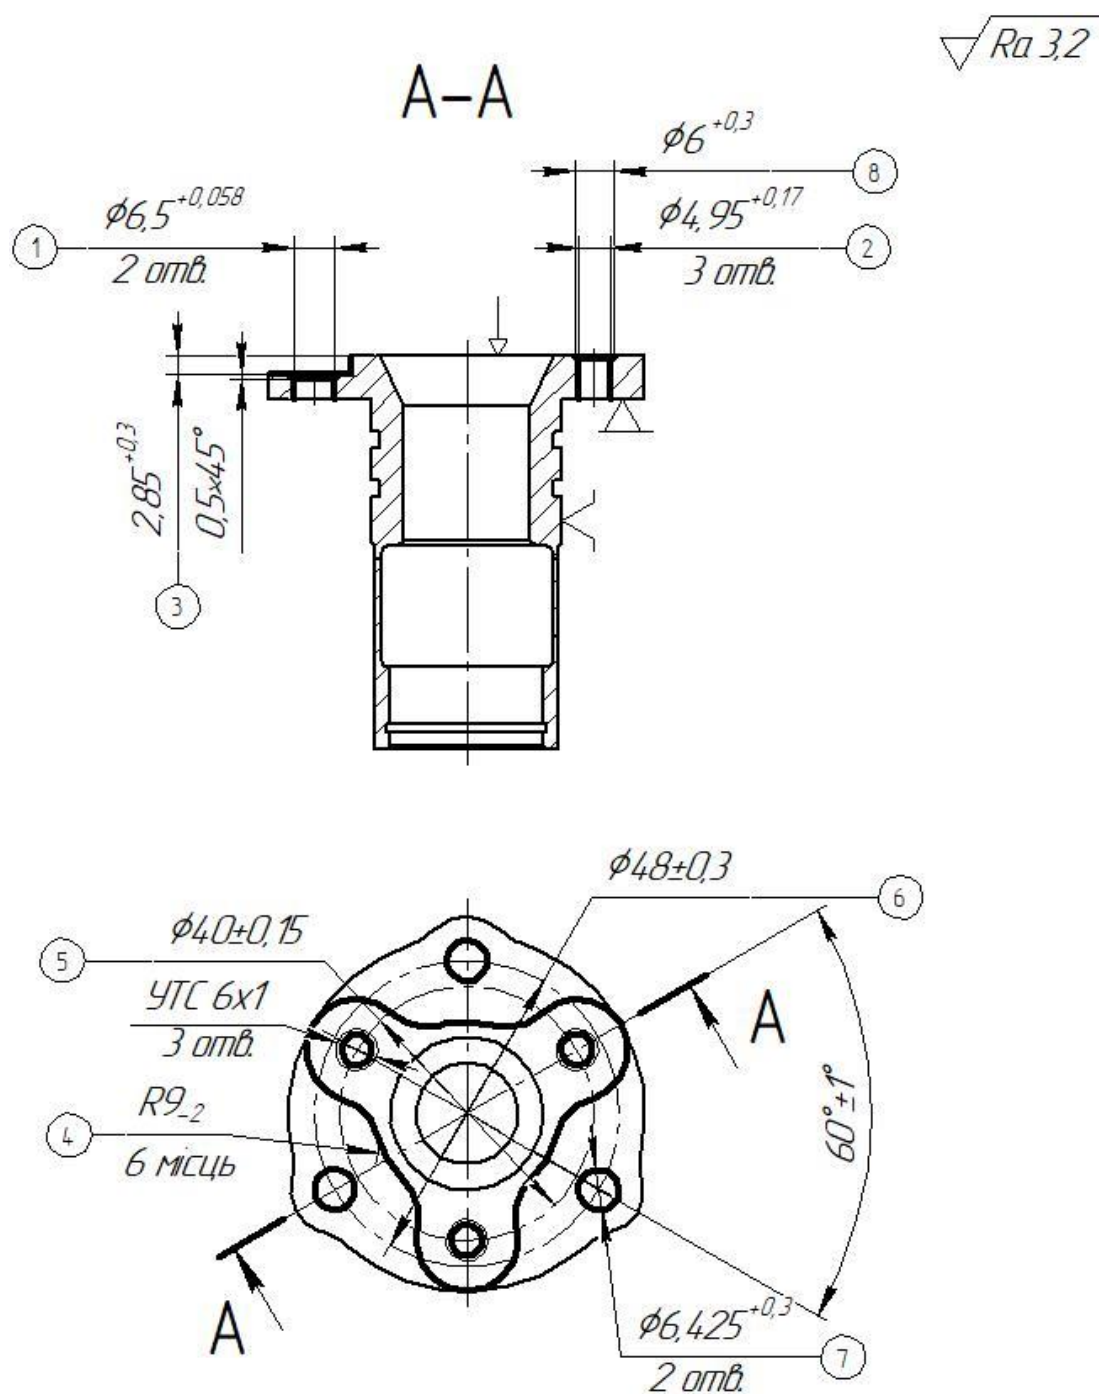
Операція 055 фрезерно-свердлильна з ЧПК
